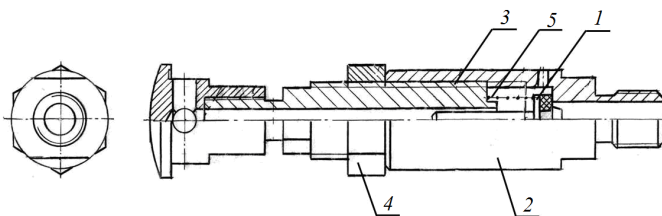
Клапан: 1 – шток; 2 – корпус; 3 – винт; 4 – гайка; 5 – пружина
